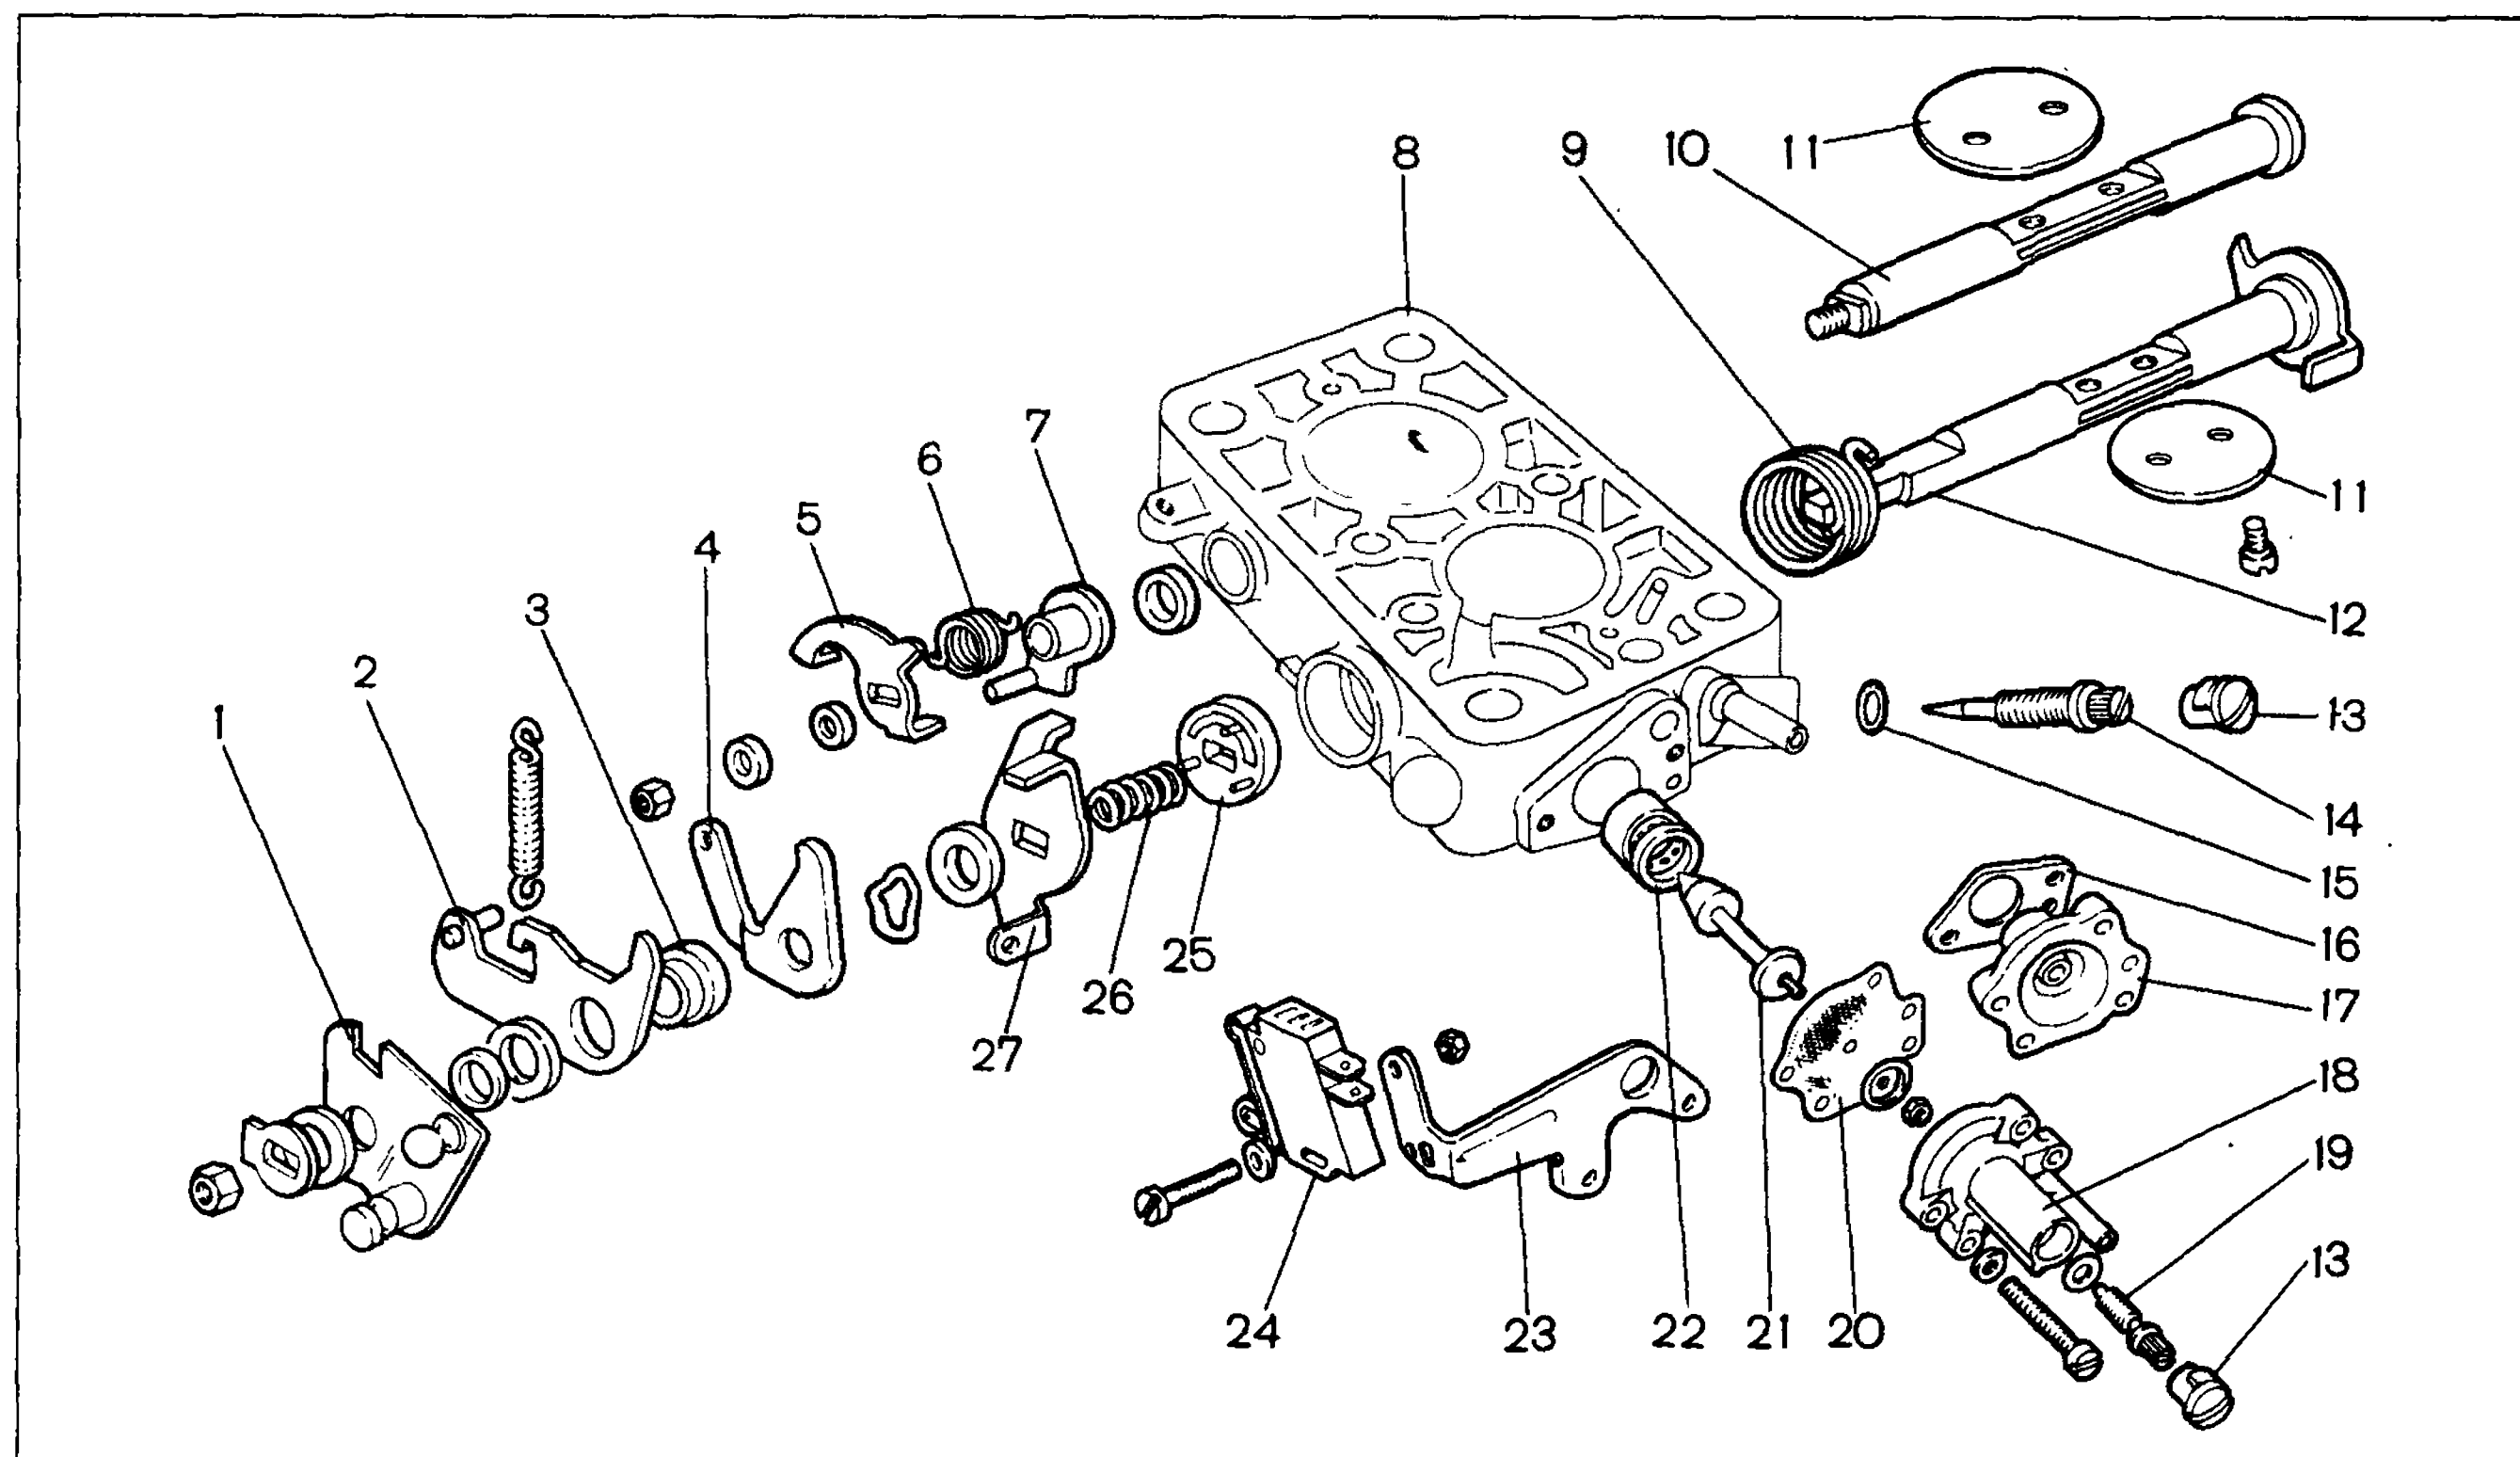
Детали корпуса дроссельных заслонок карбюратора 2107-1107010:
